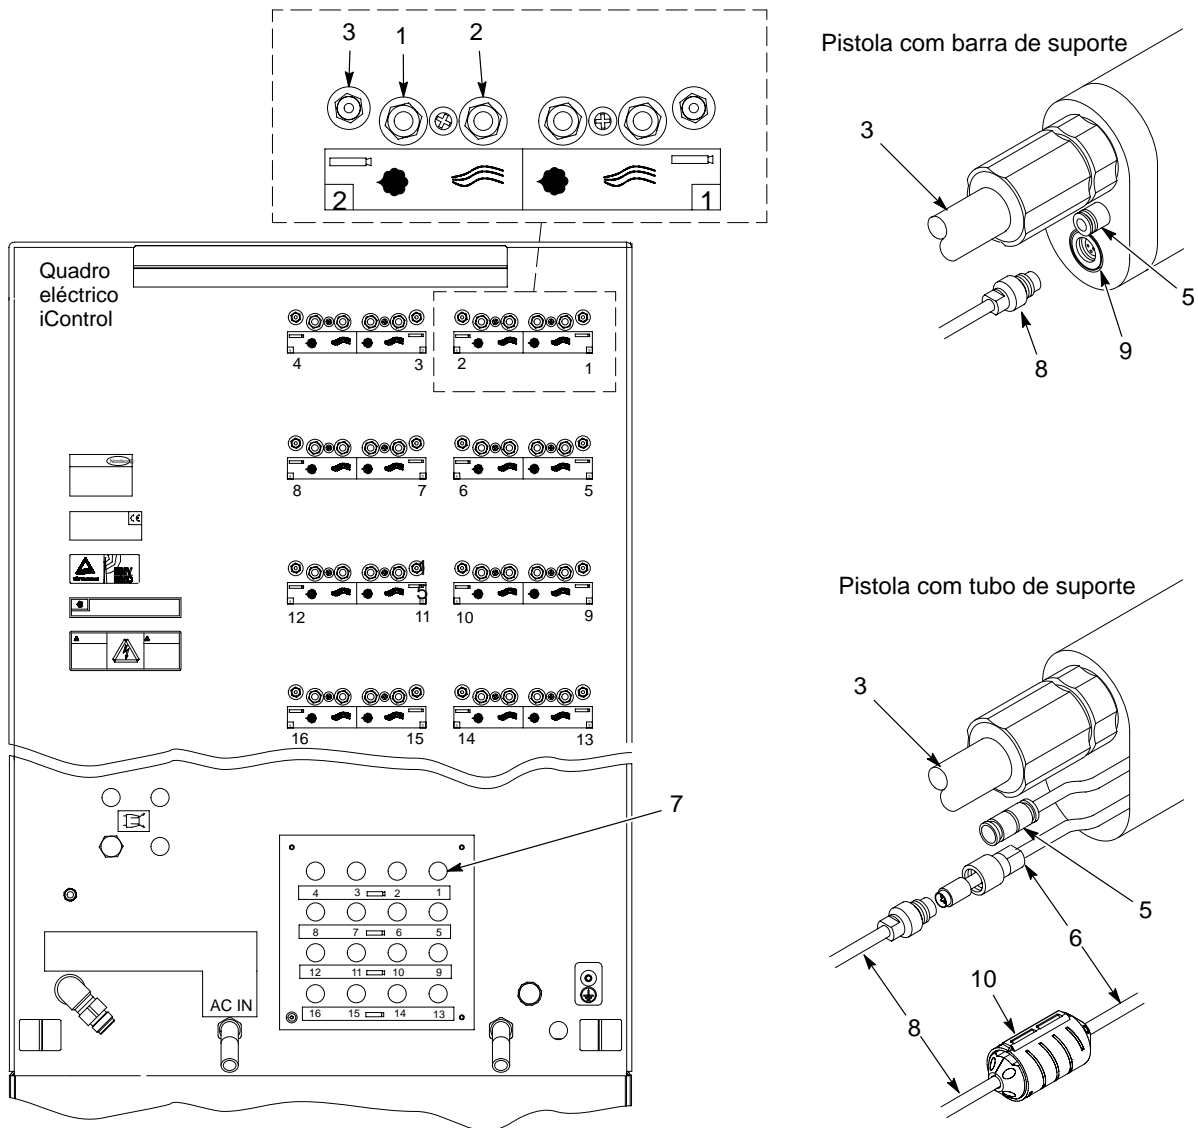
Montagem do cabo e dos tubos de ar da pistola
